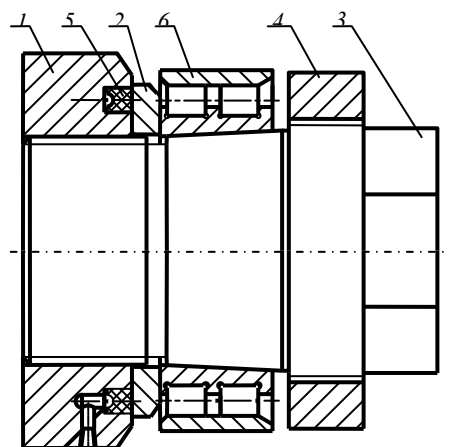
Устройство регулирования радиального зазора крупных подшипниковых узлов: 1-регулирующая гидрогайка; 2-промежуточное кольцо; 3-шпиндель; 4-компенсирующее кольцо; 5-манжета; 6-подшипник
